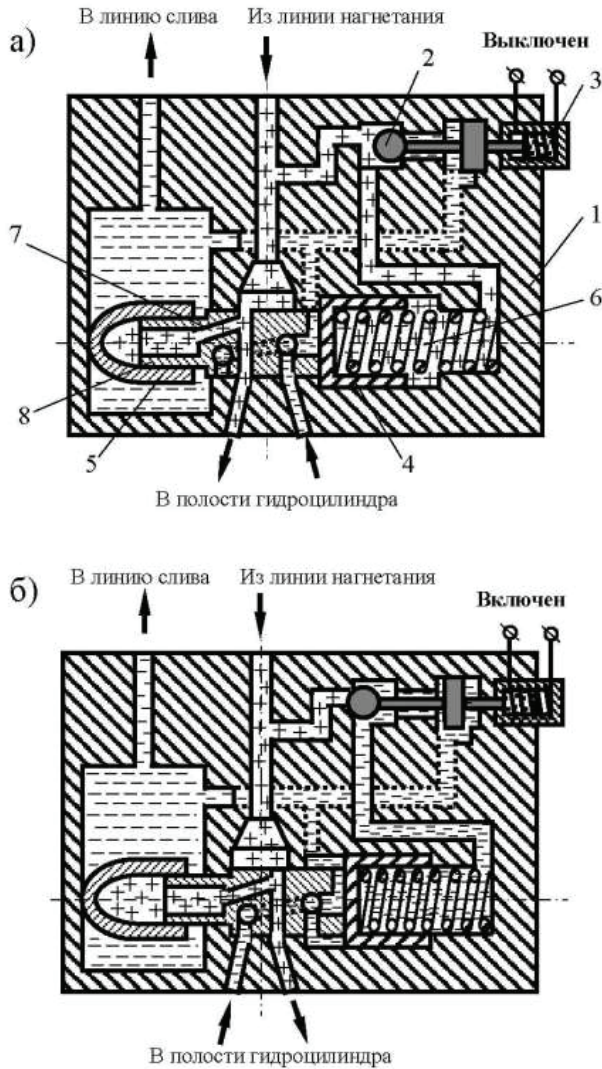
Принципиальная схема электромагнитного клапана, где 1- корпус; 2- шариковый клапан; 3- электромагнит; 4, 5- поршни; 6- пружина; 7- отверстие в золотнике; 8- золотник
